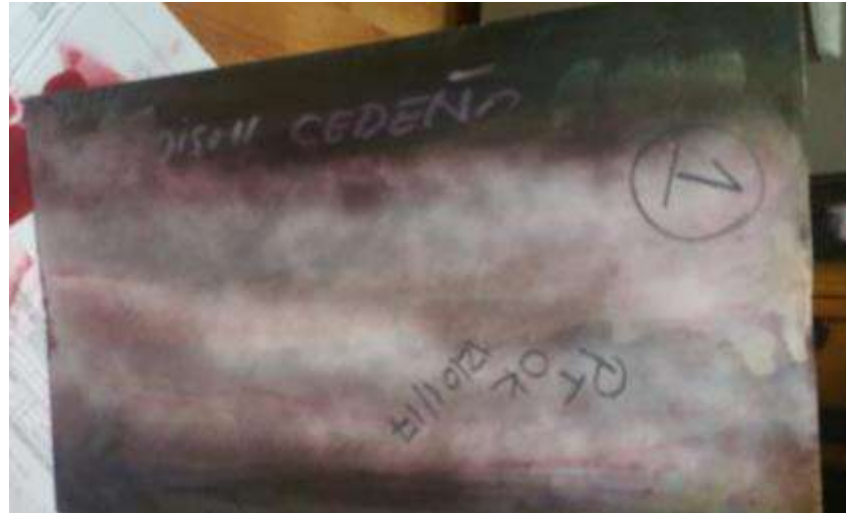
Inspección por líquidos penetrantes, técnica visible efectuada para la placa de 6mm
